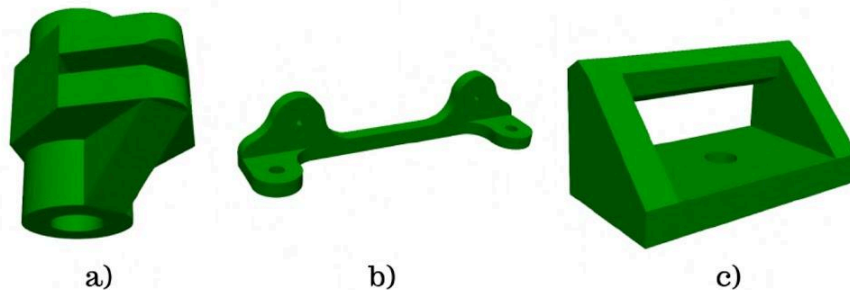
Peças de impressão 3D fabricadas a) suporte para barra roscada; b) suporte para instalação do; c) Suporte para alça
